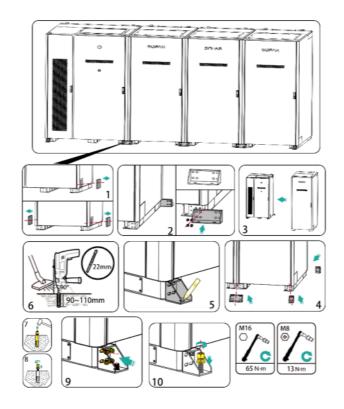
Schema di installazione dell'armadio di accumulo dell'energia e collegamento dell'armadio della batteria
